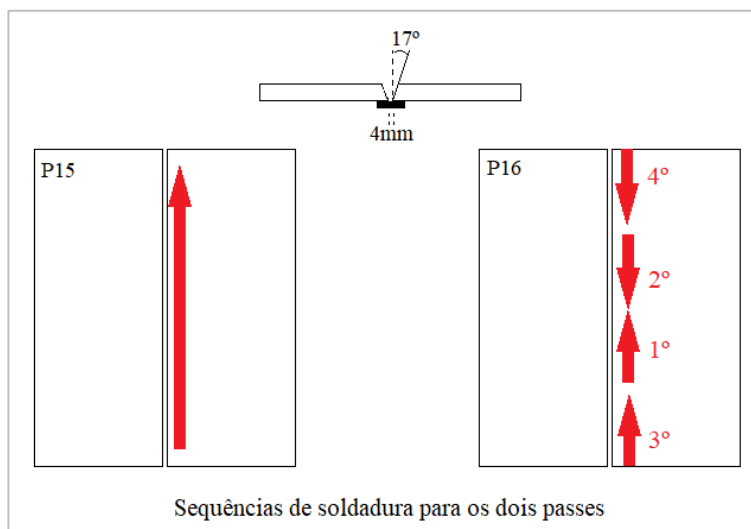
Sequências de soldadura seguidas nos provetes P.15 e P.16 (Fonte: West-sea)
